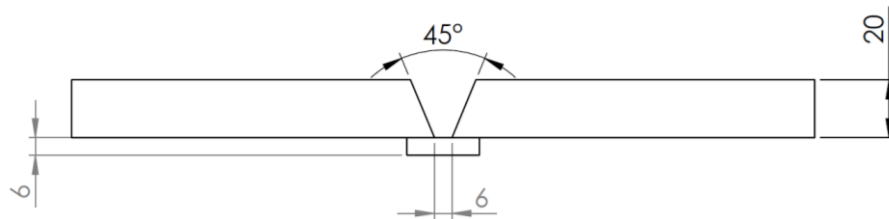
Diseño de junta de soldadura. Fuente: Autor
